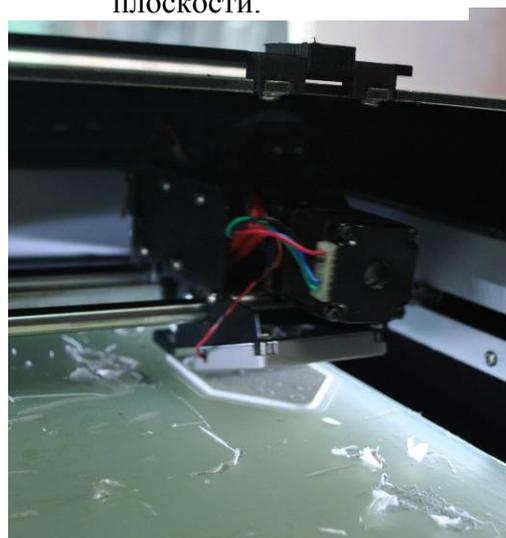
Изготовление деталей на 3D-принтере PICASO 3D Designer.
